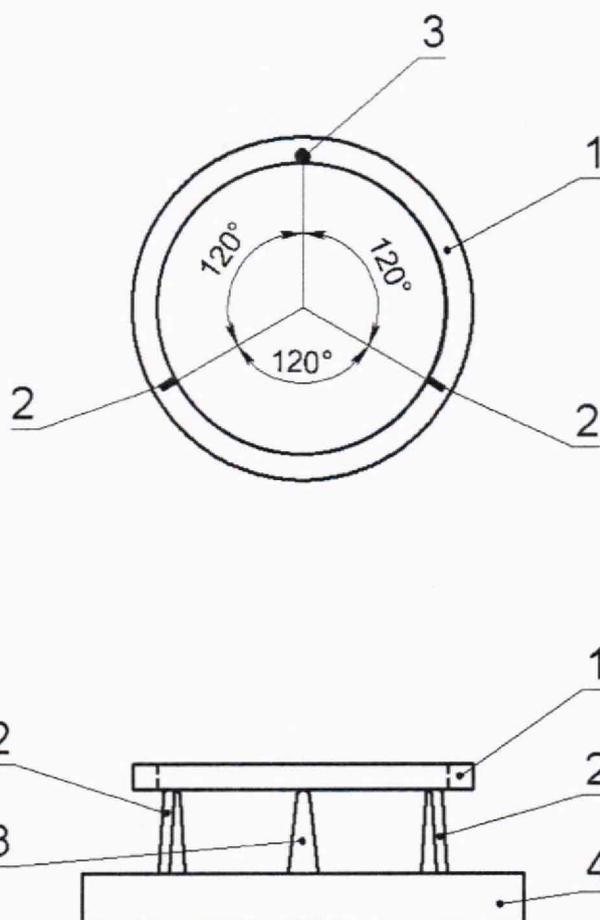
Схема установки образца диска специального на призмы компарирующего устройства и приспособление-опору
